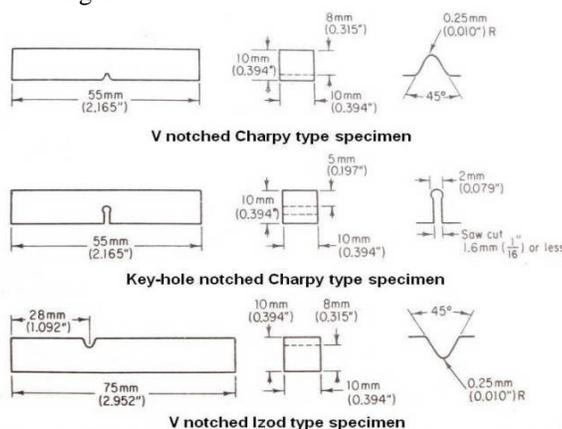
Dimensiones y ángulos de la muestra que se utilizó para basarse en la máquina muescadora.
